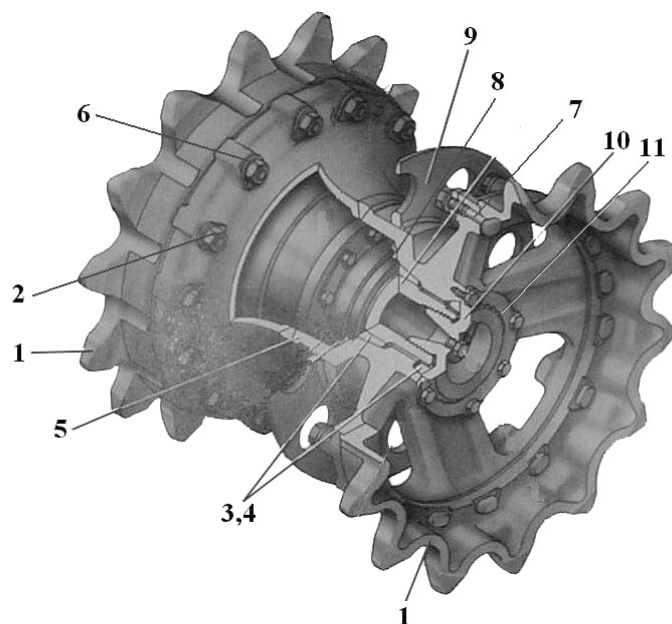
Ведущее колесо: 1 – венец; 2 – гайка; 3, 4 – конусы; 5 – диск ведущего колеса; 6 – стопорная шайба; 7 – болт; 8 – кольцо лабиринтного уплотнения; 9 – ограничительный диск; 10 – пробка; 11 – зубчатая шайба
